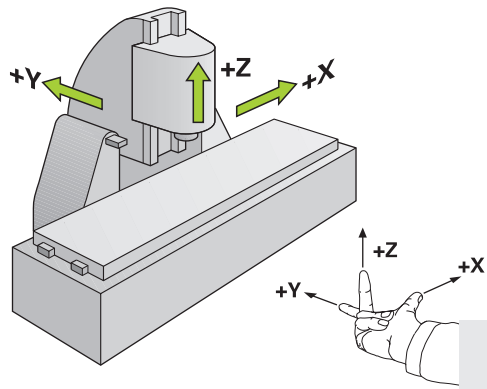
Привязка прямоугольной системы координат к осям станка
